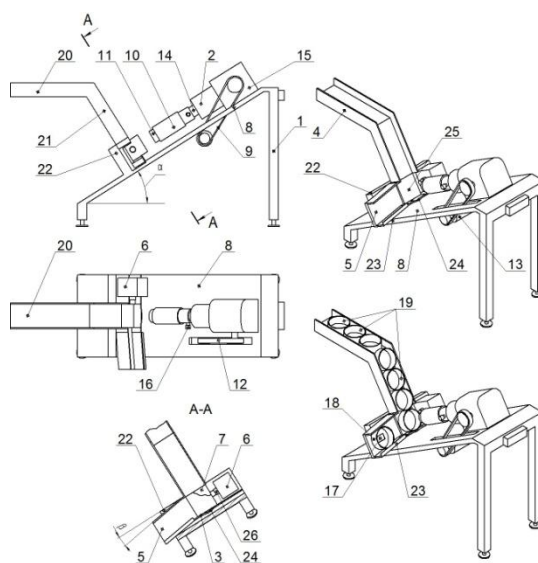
Машина для маркировки на дне цельнотянутых или сборных с доннышком металлических корпусов консервных банок:
